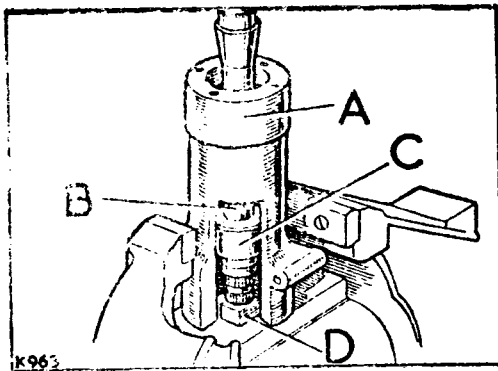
Caja compensadora, eje y taco de apoyo en su posición correcta.
